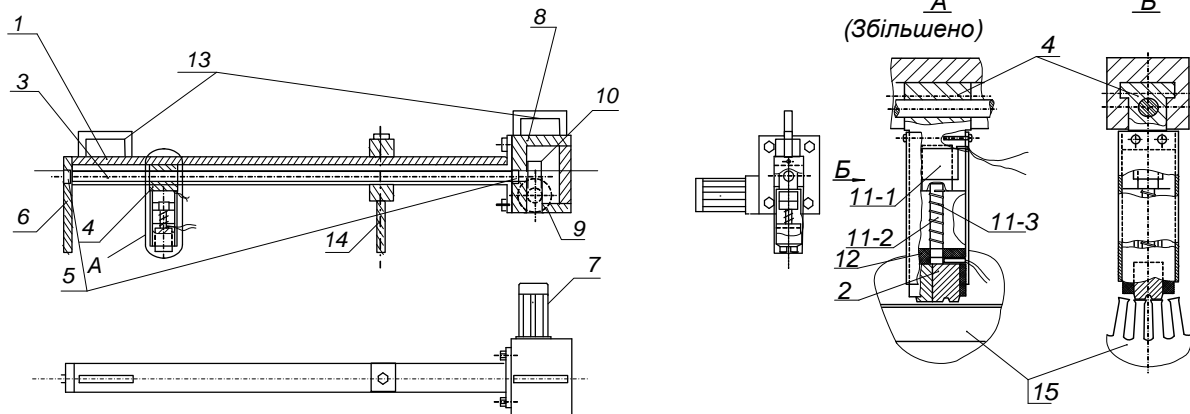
Загальний вигляд механічної частини АСЛТ
